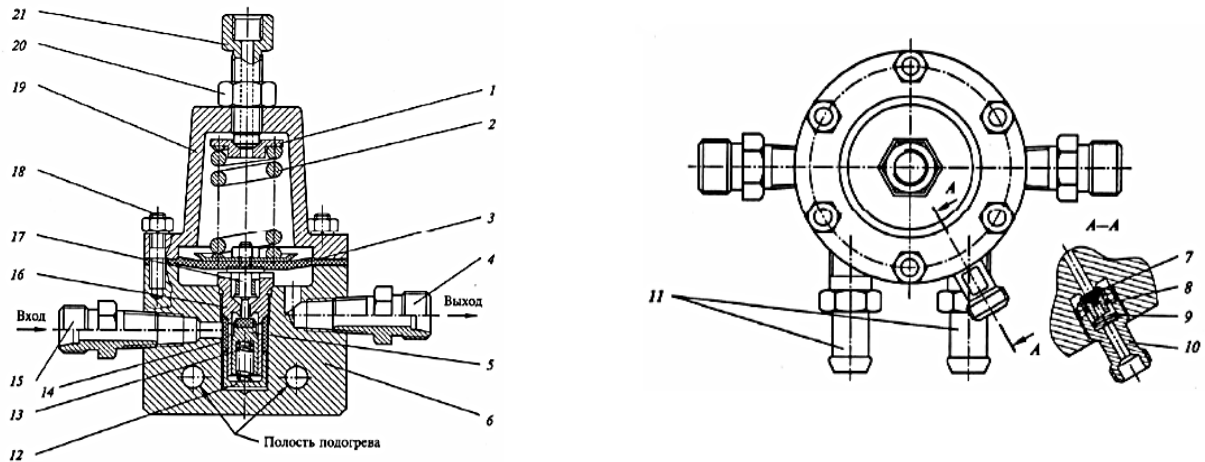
Редуктор высокого давления РЗАА: 1 - упор пружины; 2 - пружина; 3 - мембрана; 4 - выходной штуцер; 5 - клапан высокого давления; 6 - корпус редуктора; 7 - вставка предохранительного клапана; 8 - предохранительный клапан; 9 - пружина предохранительного клапана; 10 - корпус предохранительного клапана; 11 - штуцеры для теплоносителя; 12 - упор клапана высокого давления; 13 - пружина клапана высокого давления; 14 - фильтрующий элемент; 15 - штуцер входной; 16 - корпус клапана высокого давления; 17 - шток мембраны; 18 - шпилька; 19 - колпак; 20 - контргайка; 21 - болт регулировочный
